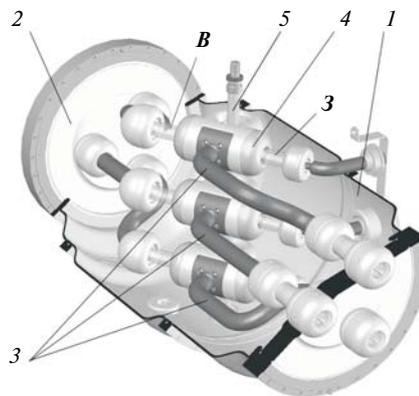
Модель разъединителя-заземлителя для КРУЭ 220 кВ: 1 – корпус; 2 – герметичный изолятор; 3 – токоведущие части; 4 – корпус подвижного контакта; 5 – изоляционный вал; В – подвижный контакт в положении «включено», З – подвижный контакт в положении «заземлено»
